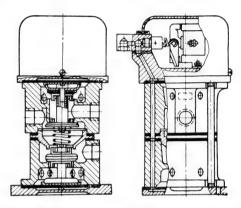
Пневматический электромагнитный мембранный клапан КПЭМ-10
